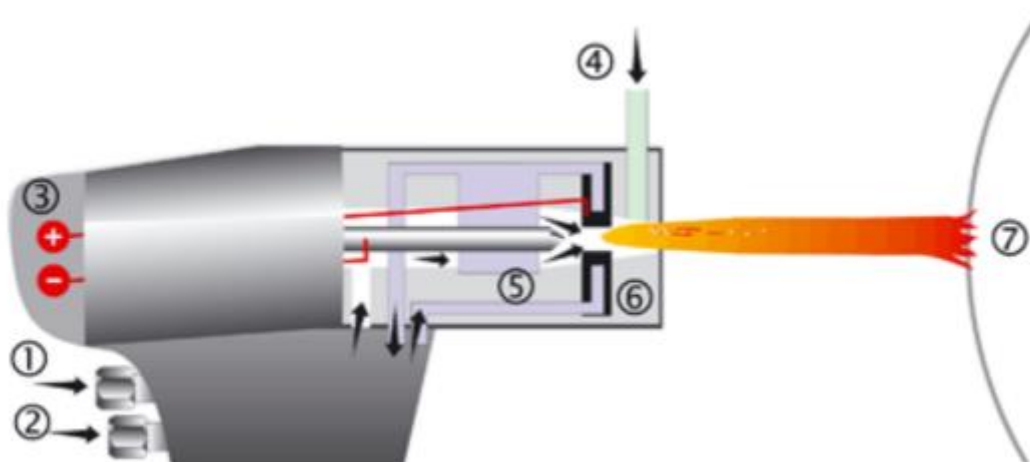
Pištolj za visokobrzinsko plameno naštrecavanje [5]
